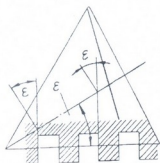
Осевой прямоугольный профиль червячной фрезы
